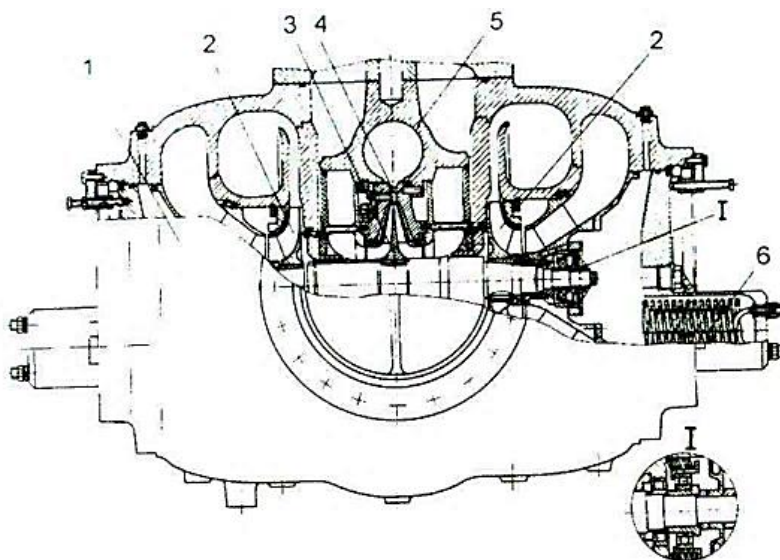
Детандер-компресорний агрегат ТКО-75/42:
